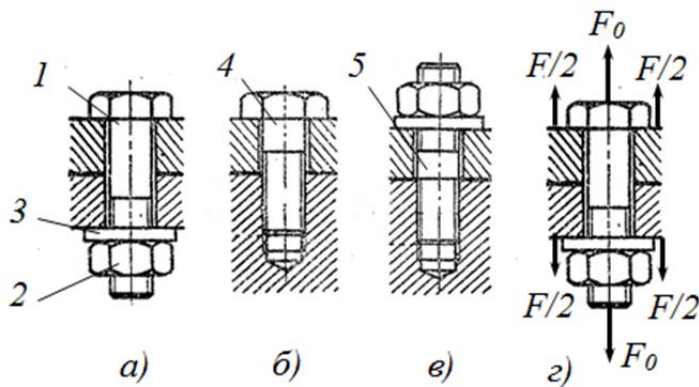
Види різьбових з'єднань: болтове (а), гвинтове (б), шпилькове (в), та розрахункова схема болтового з'єднання (г);
